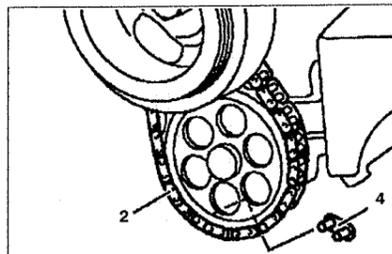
Соедините концы новой цепи 2 с помощью нового промежуточного звена 4.
